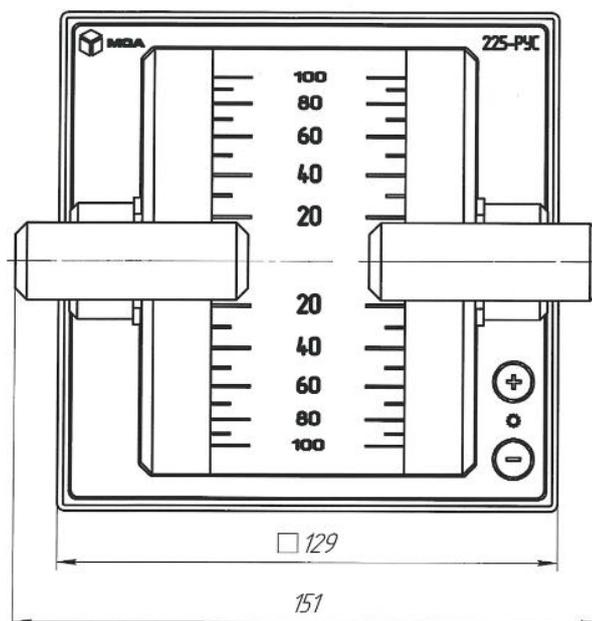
Габаритные размеры изделий типа РУС-225
